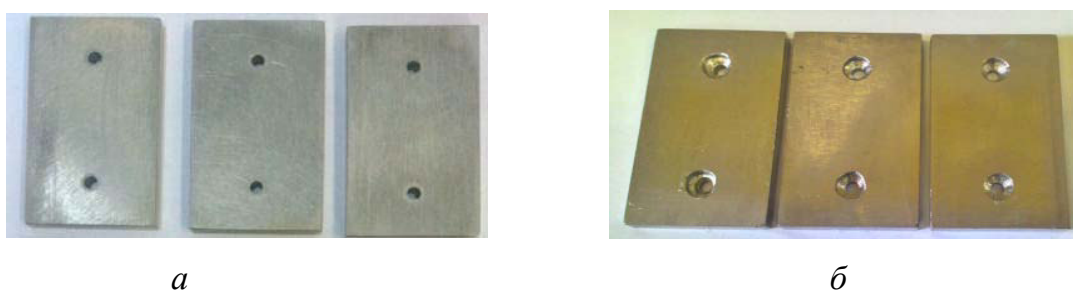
Образцы на струевую коррозию до испытаний (а) и после испытаний (б) металла, наплавленного сварочной проволокой марки Св-МНЖМцТК40-1-1-0,3-0,1
